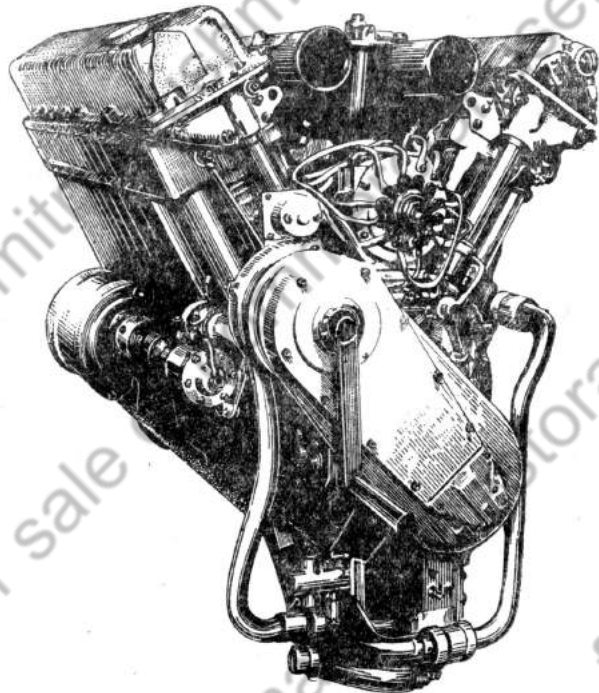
Общий вид двигателя тяжелого танка (вид со стороны передачи, левая сторона)
